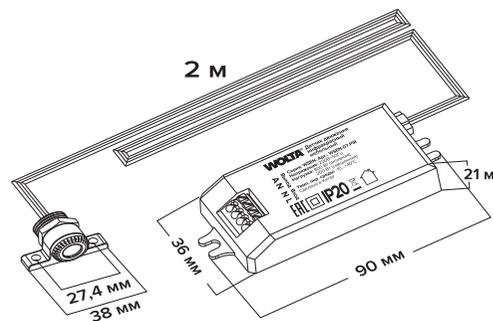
Габаритные размеры датчика WSEN-07-PIR
